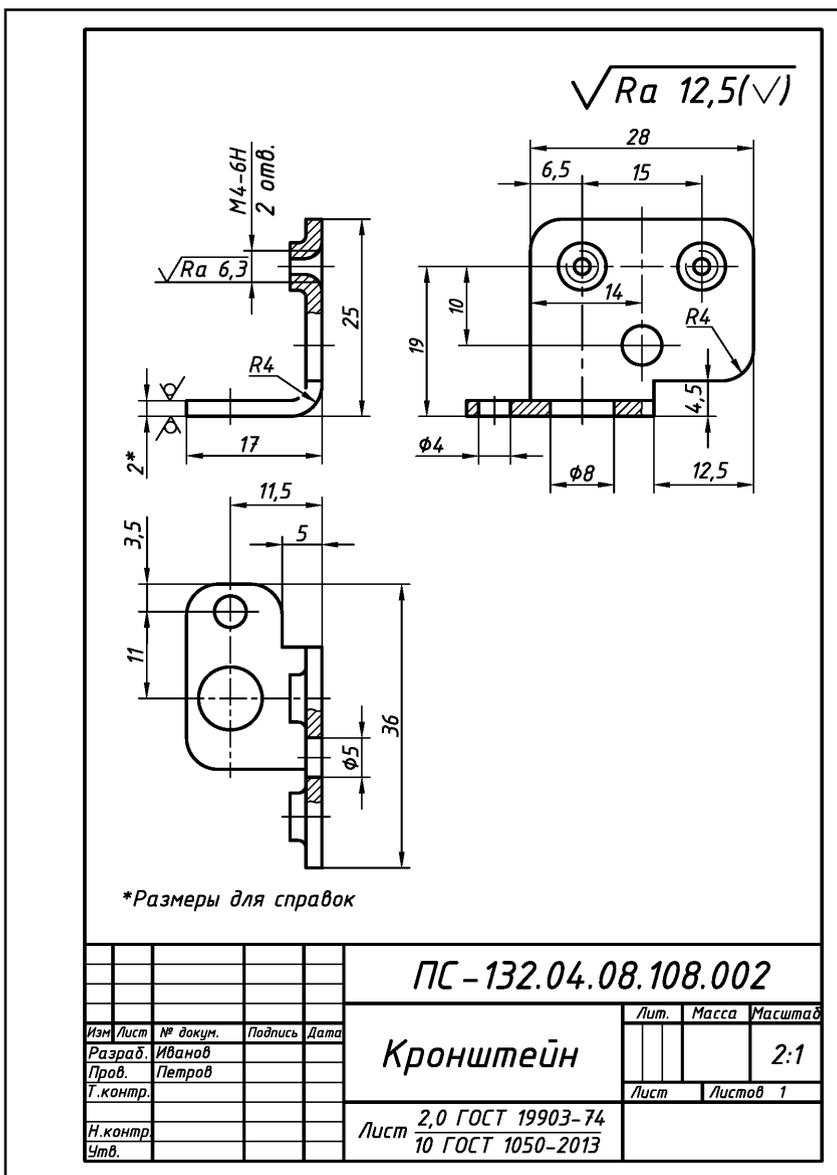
Оформление рабочего чертежа гнутой детали из тонколистового металла
